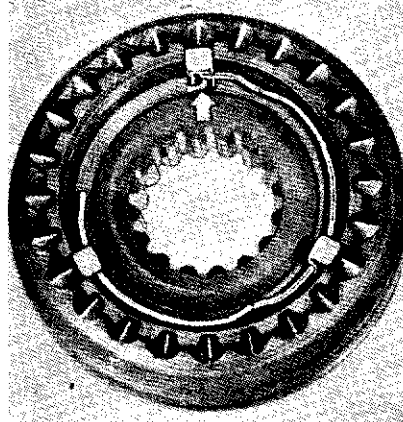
Positionnement des ressorts d'arrêt des clavettes
